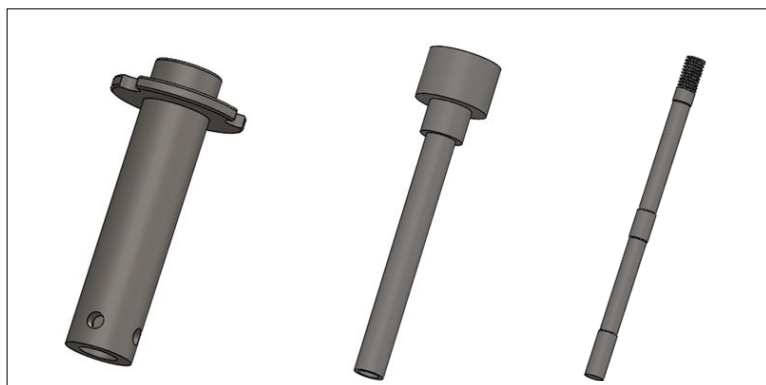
rendu 3D d'outils RFSSW pour notre machine
